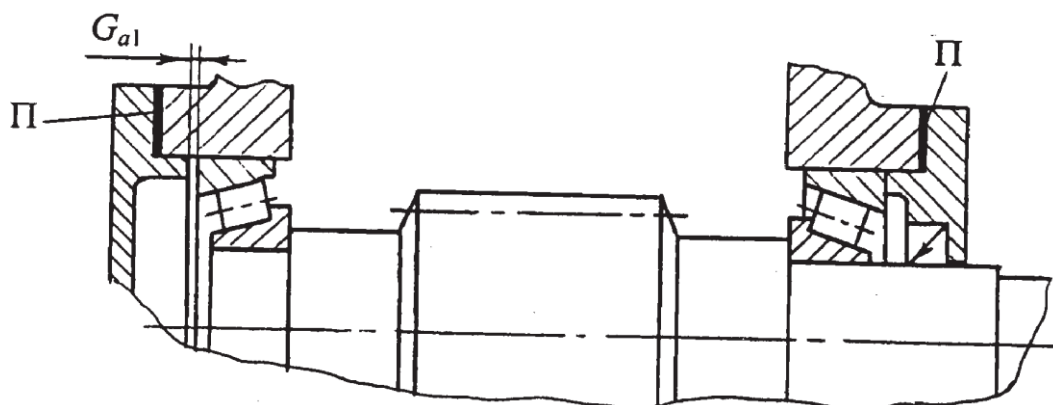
Установка червяка на двух радиально-упорных подшипниках: П — регулировочные прокладки
